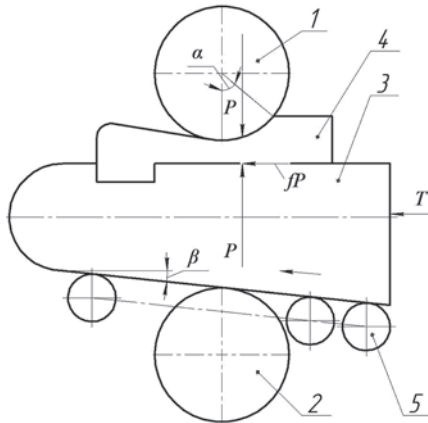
Схема обжатия полосы на оправке с параллельной к направлению прокатки калибрующей поверхностью: 1 – рабочий валок; 2 – опорный валок; 3 – оправка; 4 – заготовка; 5 – направляющие ролики
